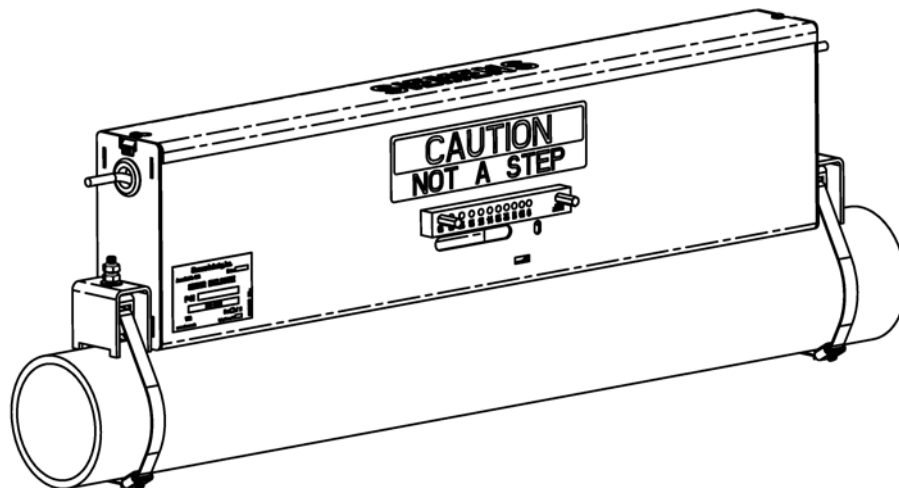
Präzisionsmontage mit einteiligem Gehäusesatz im eingebauten Zustand
